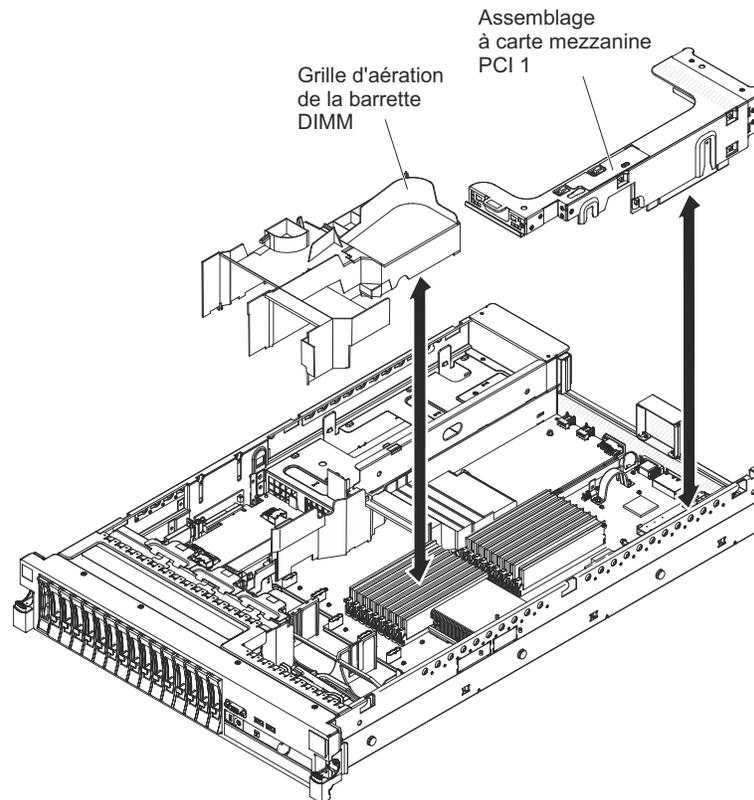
Retrait de la grille d'aération des barrettes DIMM
